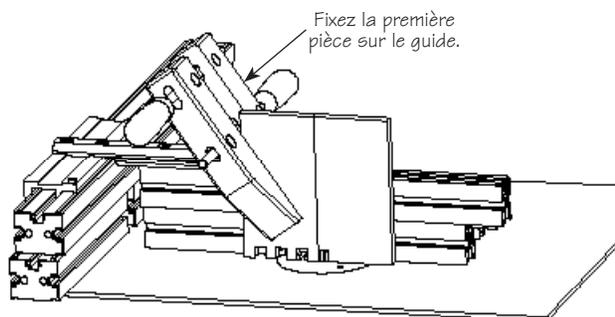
Usinage de la deuxième pièce pour l'assemblage à queues droites.
